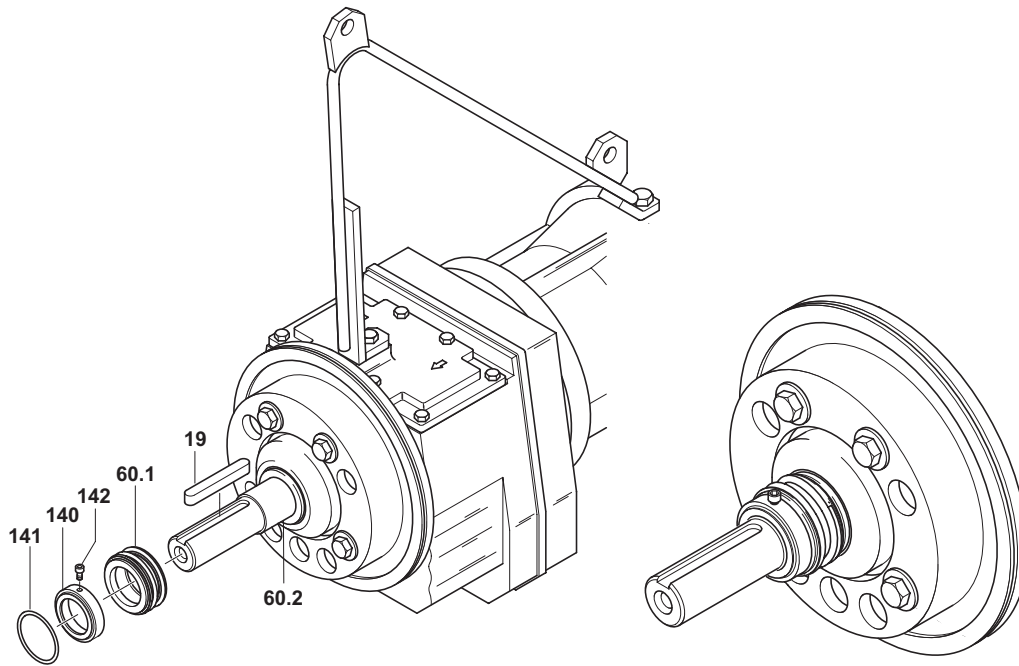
Montaje de la junta mecánica SB, XSB900, XSB 2500
